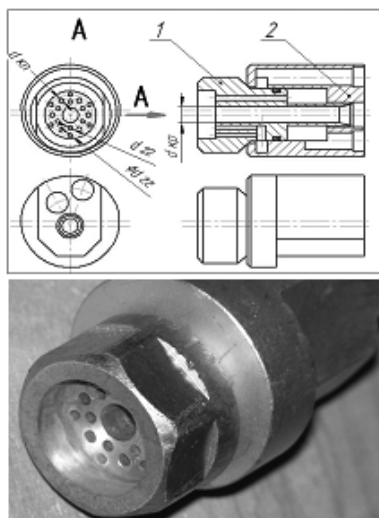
Модуль 6.5. Головка в сборе резака для кислородной резки высоколегированных сталей и чугуна толщиной до 1000 мм – сверху; общий вид головки в сборе резака Р7-ФЛЦ – внизу
